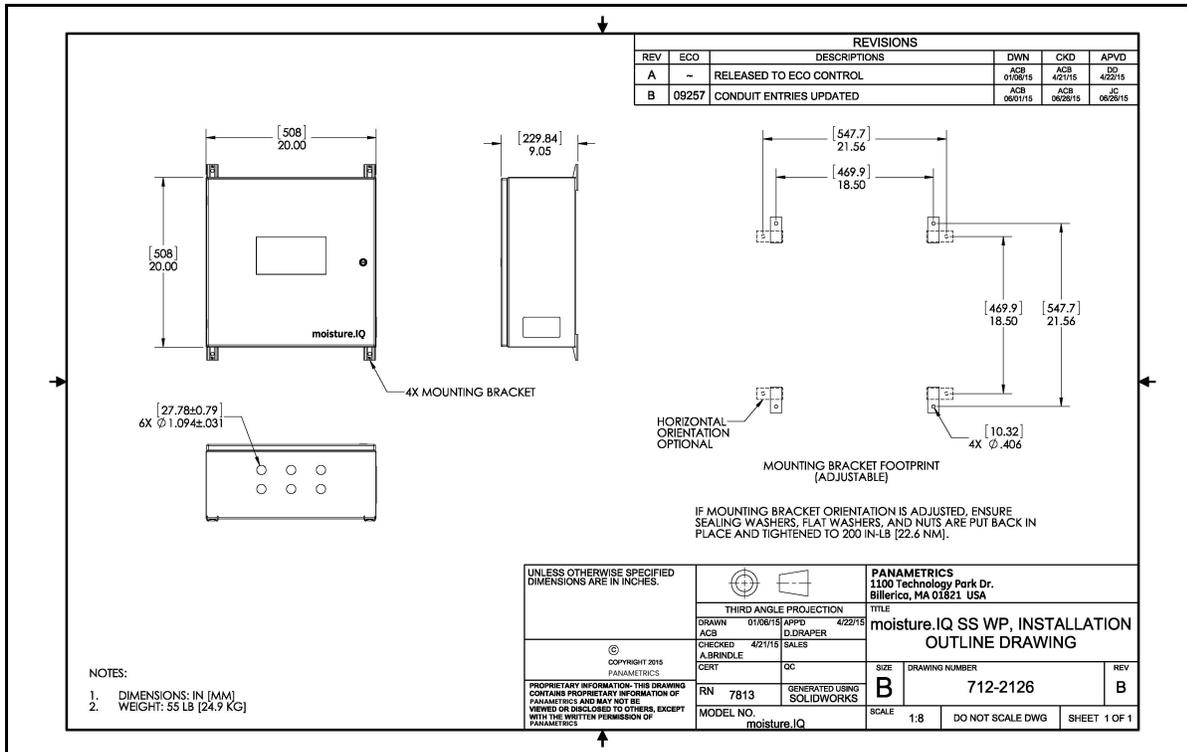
Umriss-Installationszeichnung für wettergeschützte Version mit Edelstahlgehäuse (Zeichnung 712-2126_revB, Blatt 1 von 1)
